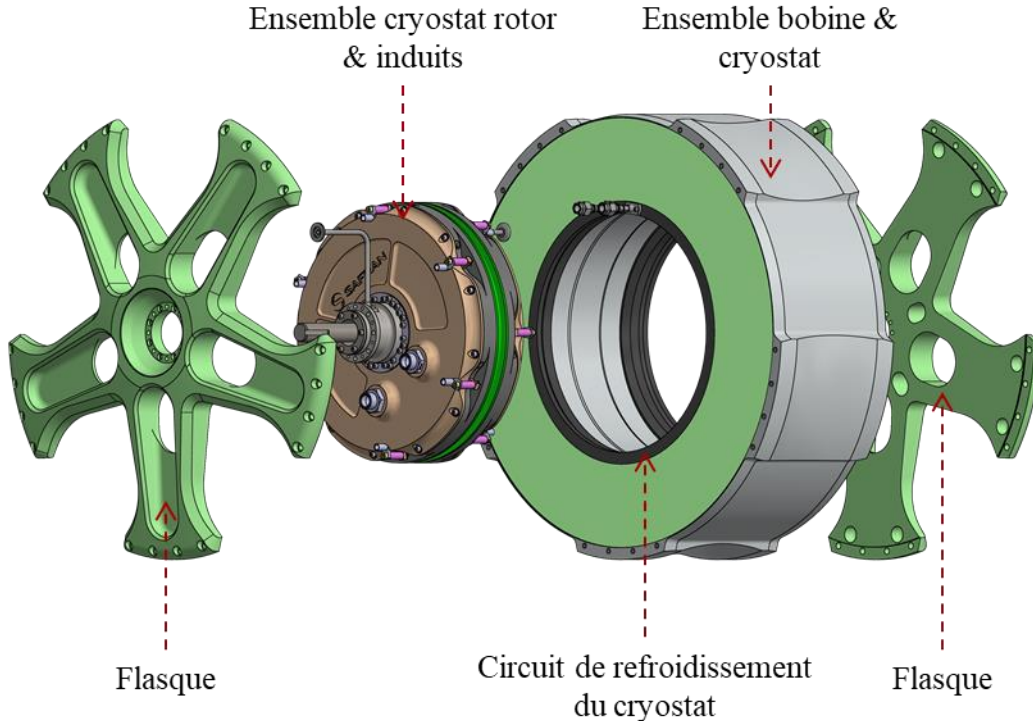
Vue éclatée des sous ensembles composant la machine.
